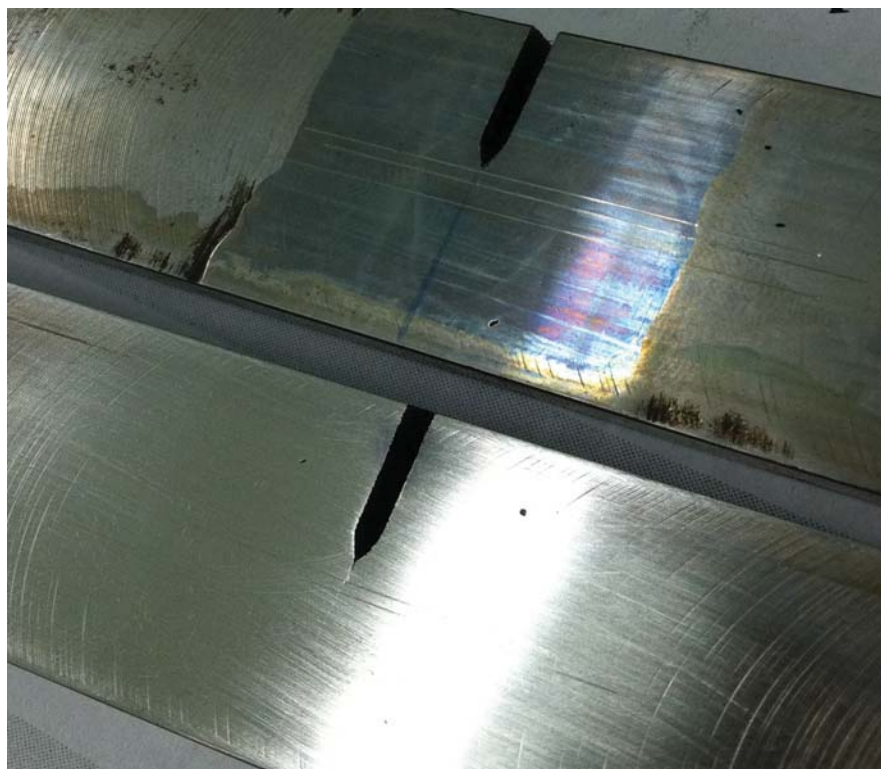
Corpos de prova SE (B) (Solda) após realização da pré-trinca
